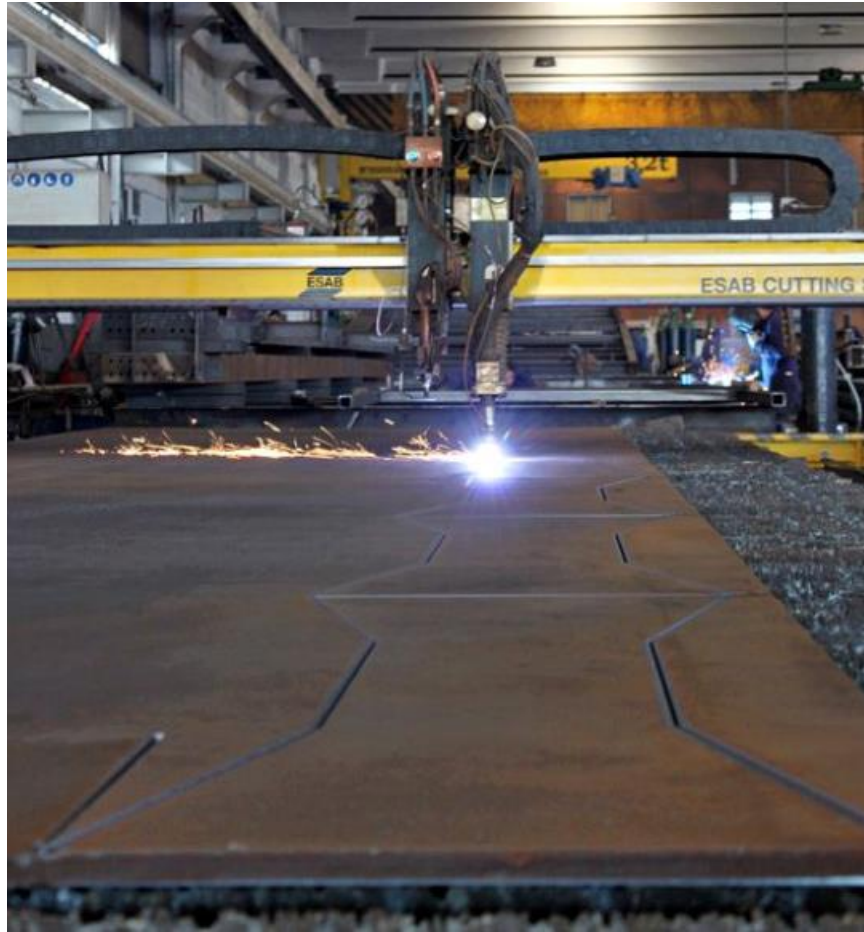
Máquina de corte de Plasma (arquivo pessoal)
